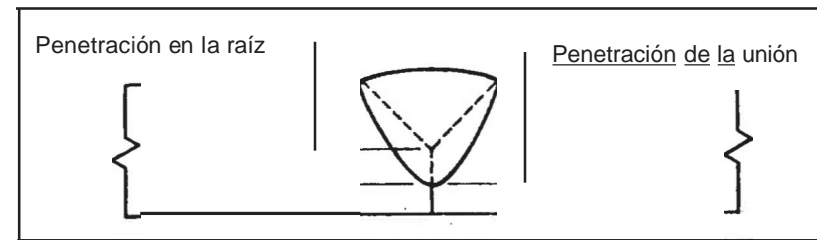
SOLDADURA CON PENETRACIÓN PARCIAL
